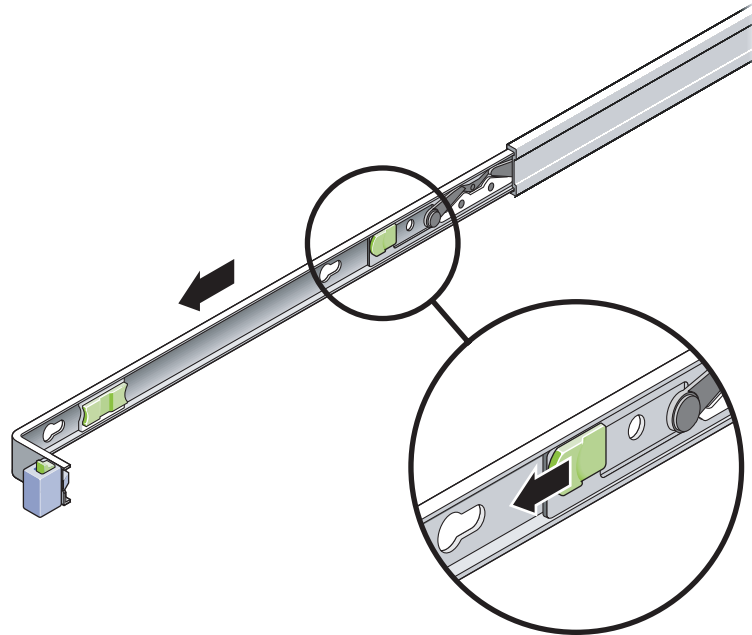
Emplacement du bouton de dégagement du support de montage
